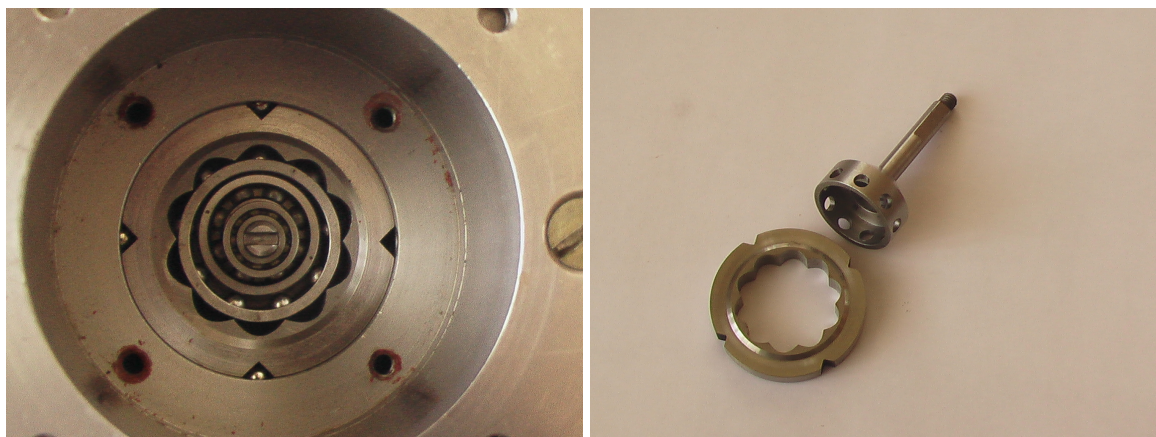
Волновая передача с промежуточными телами качения (слева в сборе, – справа жесткое колесо и обойма с пазами)
